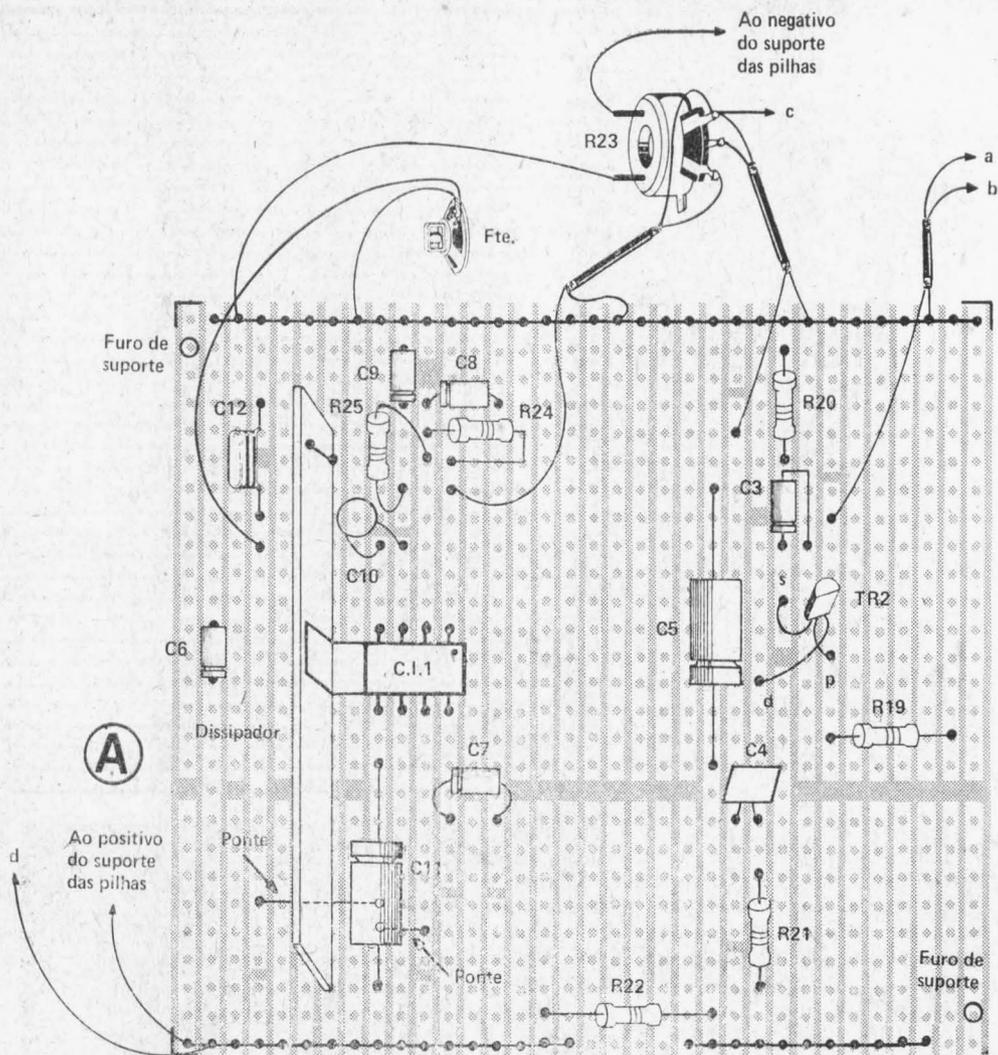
(A e B) — Disposição dos componentes sobre as plaquetas da Fig. 2 (A e B, respectivamente).
